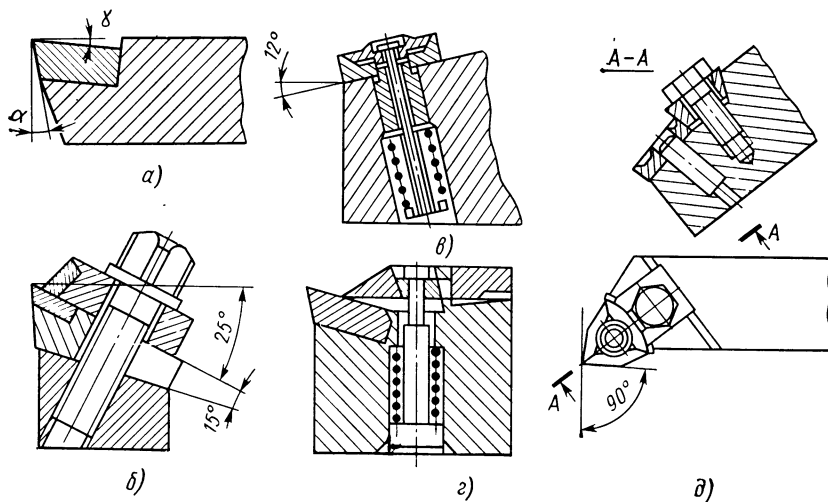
Конструкции резцов при различных способах крепления режущих пластинок:
